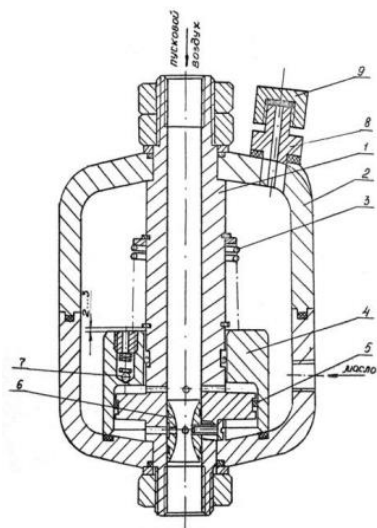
Устройство масловпрыска: 1 – стержень; 2 – резервуар для масла; 3 – пружина; 4 – поршень; 5 – уплотнительные кольца; 6 – диффузор; 7 – клапан; 8 – штуцер; 9 – заглушка
